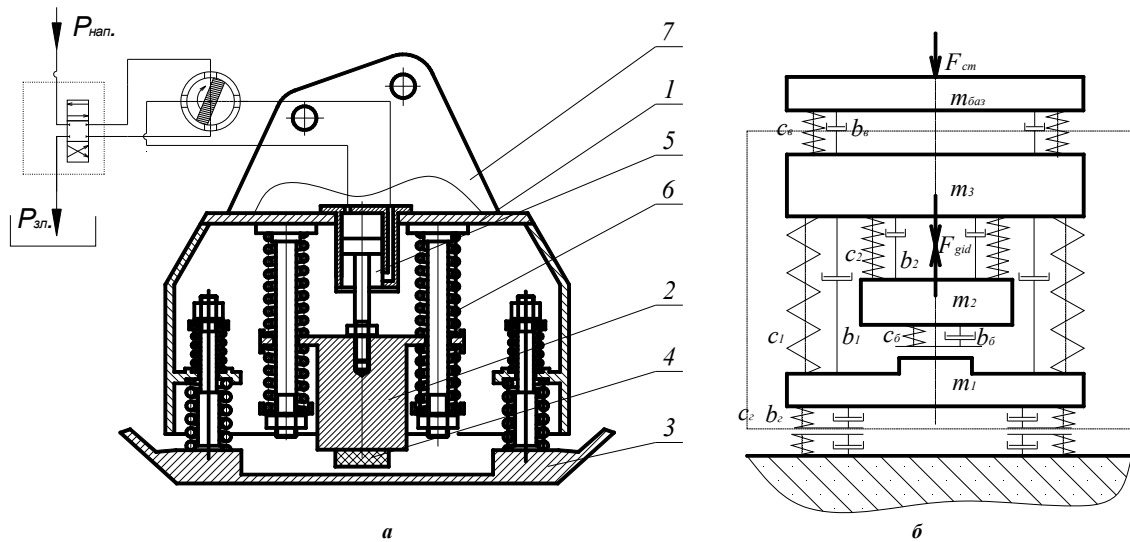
Гідравлічна віброударна трамбівка: а) конструктивна схема; б) розрахункова схема
